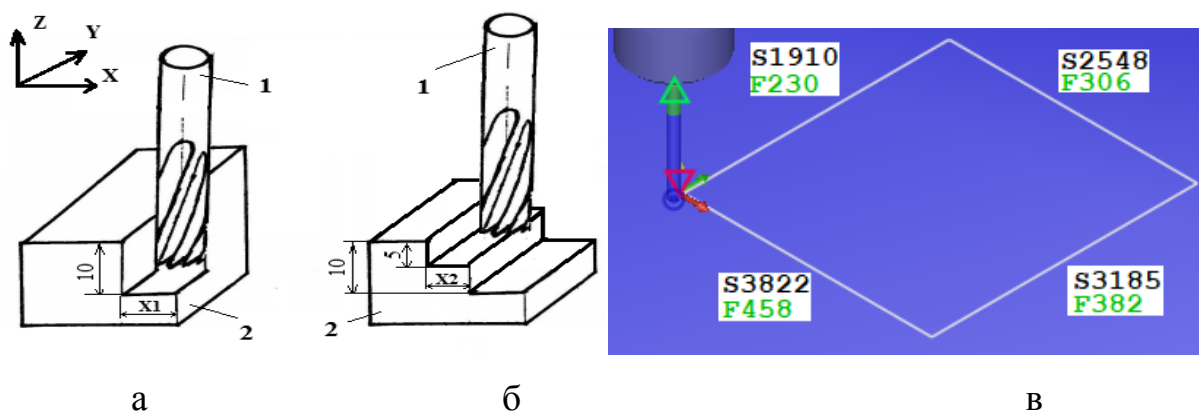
Траектория движения инструмента: 1 – фреза; 2 – заготовка; а – ширина фрезерования 10 мм; б – ширина фрезерования 5 мм; в - схема обработки детали по контуру (изометрия)
